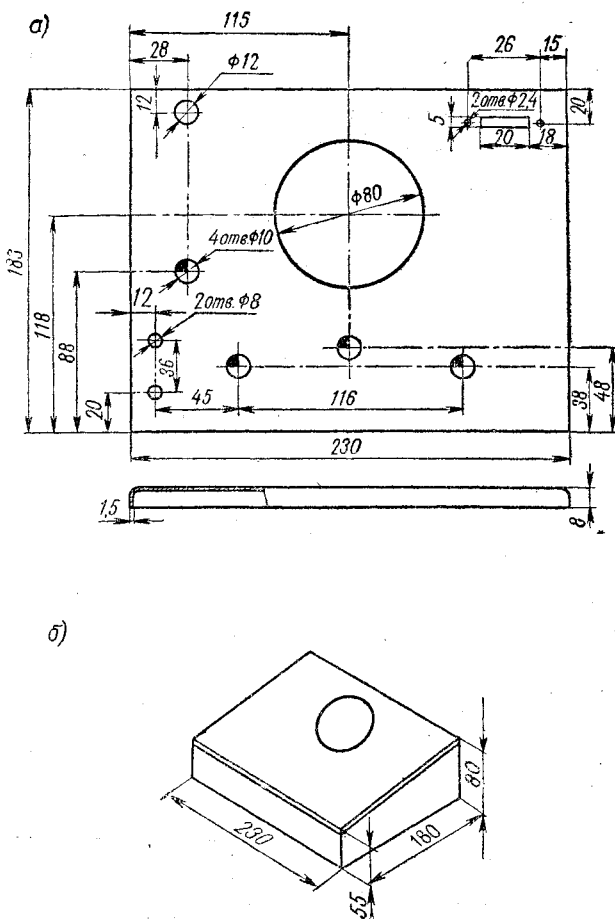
Корпус прибора: а — передняя панель, б — сборочный чертеж.
